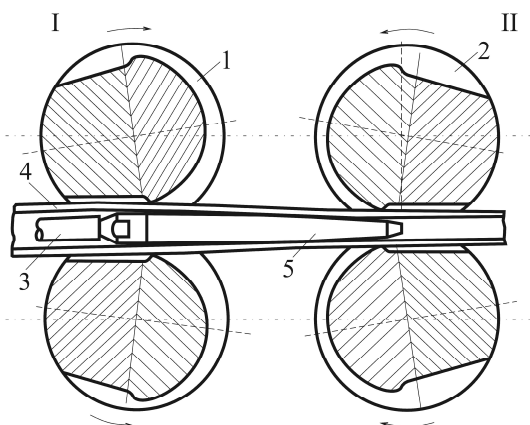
Кинематическая схема стана холодной прокатки труб: 1 – калибр с ручьем переменного сечения; 2 – зев калибра; 3 – стержень; 4 – труба; 5 – коническая оправка
